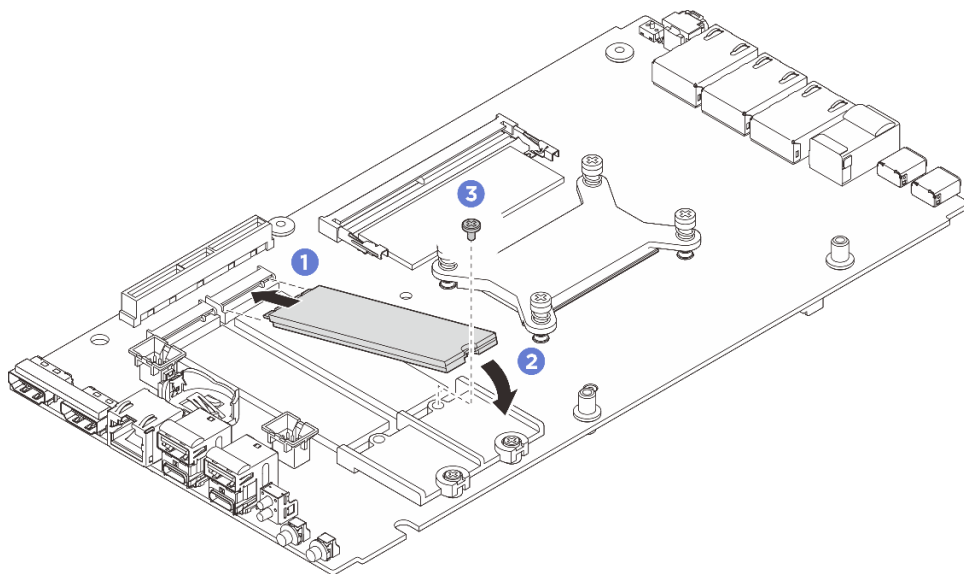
Installieren des M.2-Laufwerkstyps 2280
